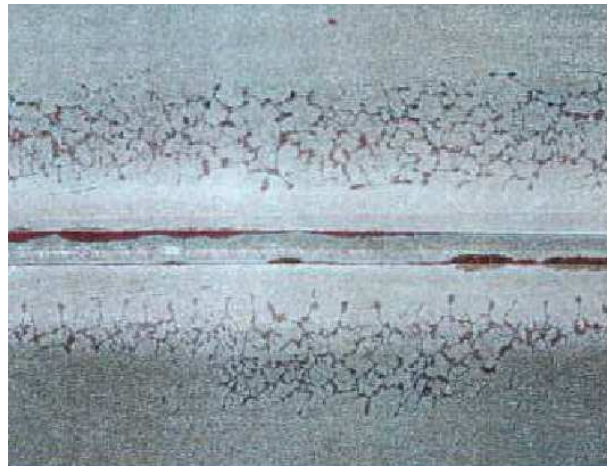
Fissuration par fatigue thermique autour d'une soudure longitudinale [86]
